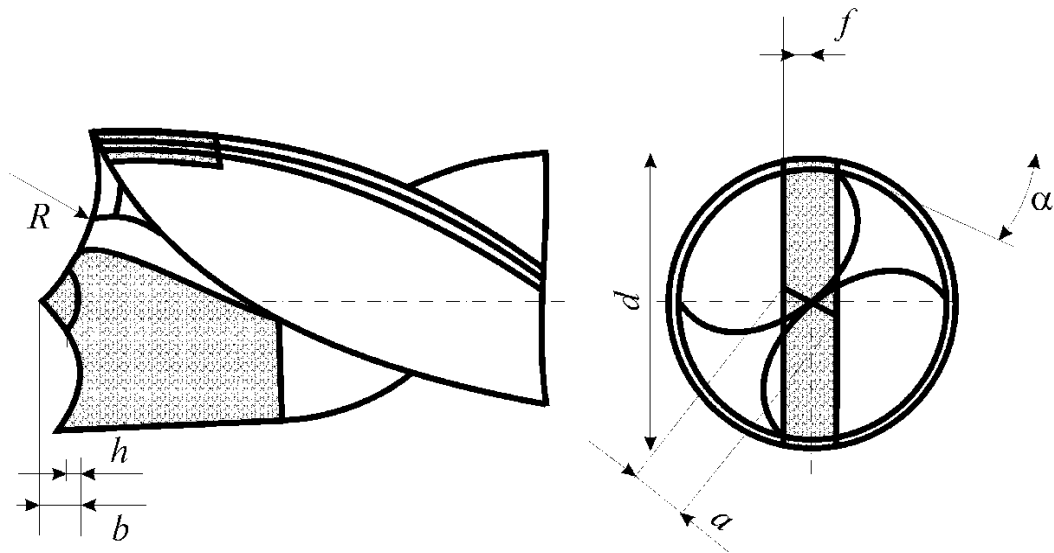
Форма заточки ріжучої частини і конструкція свердла з твердого сплаву: спіральна форма ріжучої частини [5]
